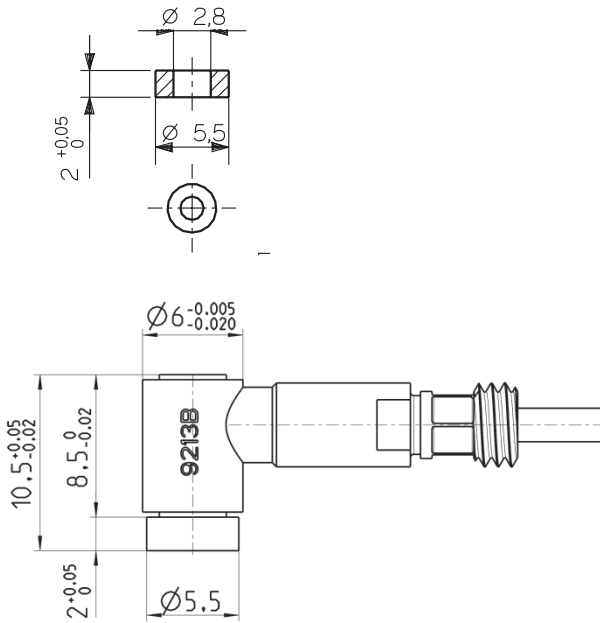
Sensor Typ 9213 mit Druckscheibe Typ 9413
